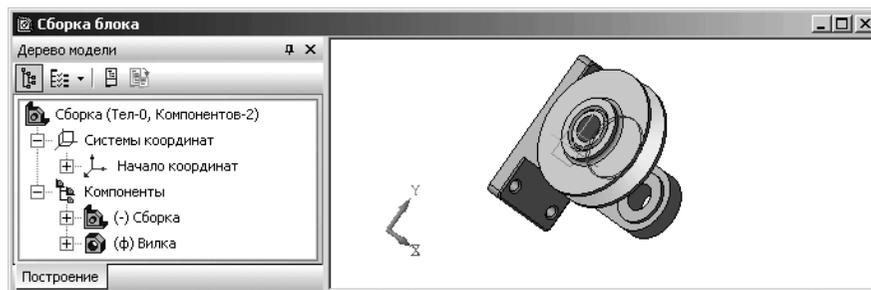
Окно Сборка\_блока с повернутыми компонентами сборки
